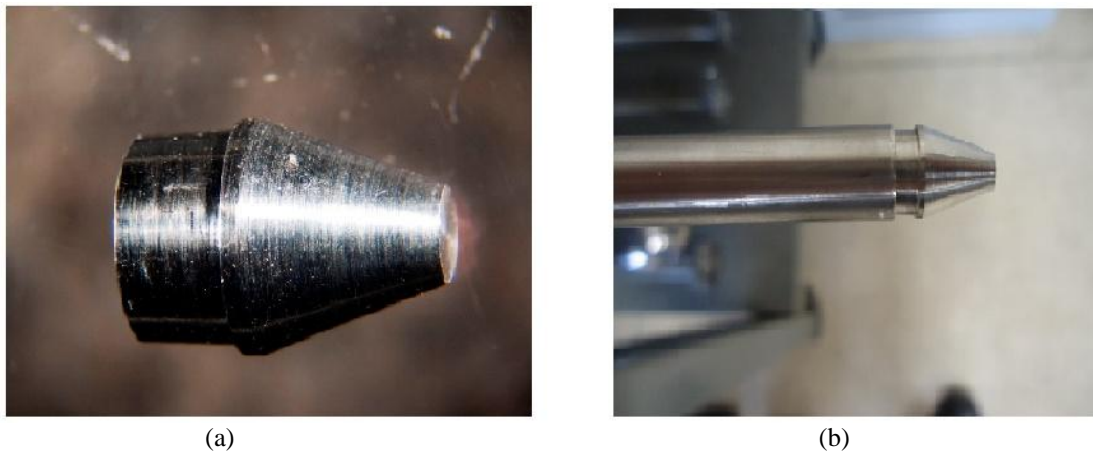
(a) Geometria do tampão utilizado e (b) Detalhe do encaixe por interferência do conjunto tampão-tubo a ser soldado. Fonte: autor.
